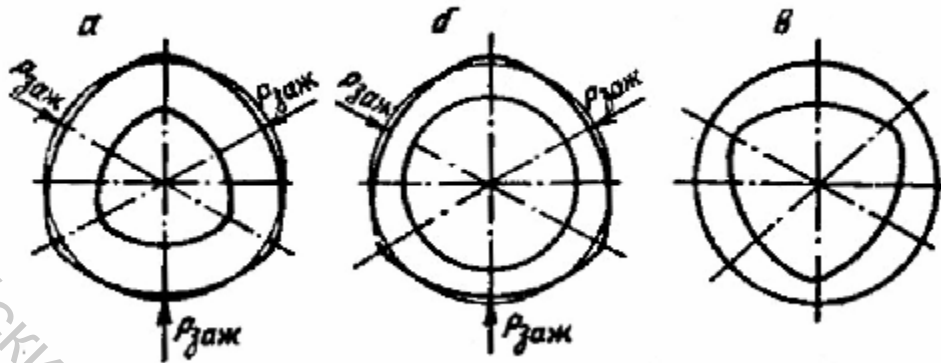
Схема формирования погрешности формы при действии зажимающих сил: а — форма заготовки после закрепления; б — форма расточенного отверстия в закрепленной заготовке; в — форма отверстия после раскрепления заготовки
